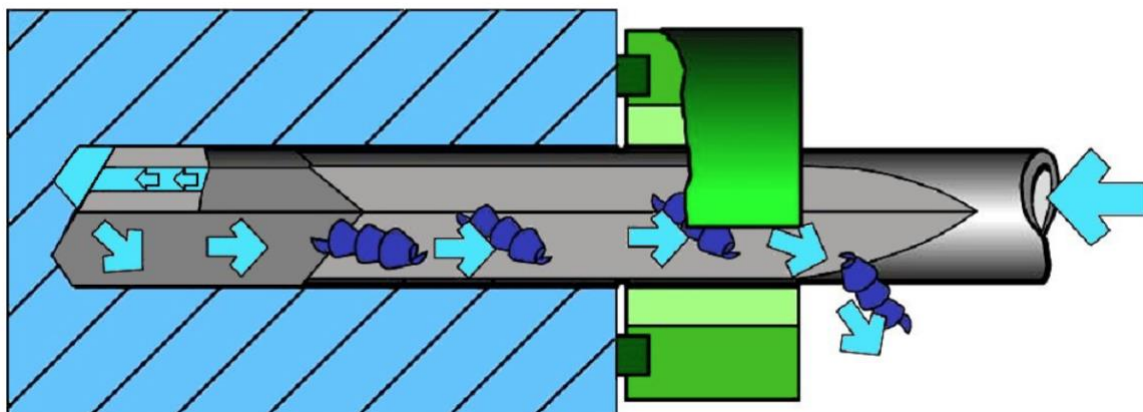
Zařízení pro ejektorové vrtání [2].
